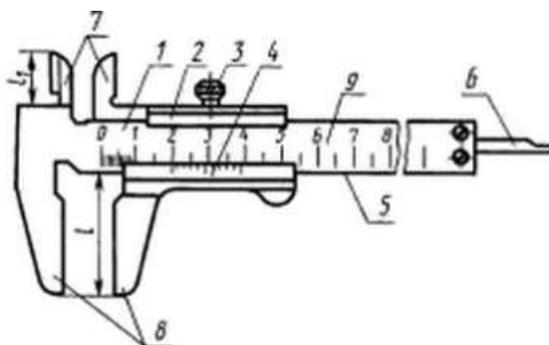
Штангенциркуль двусторонний с глубиномером
